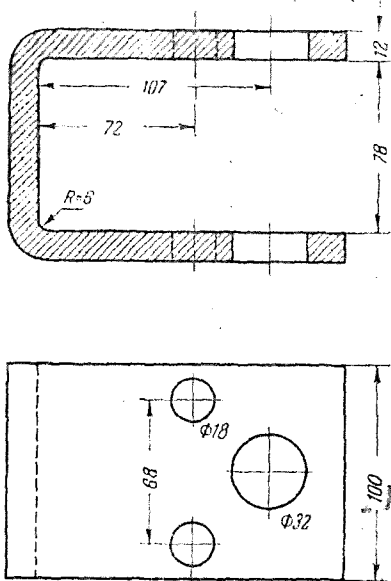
Скоба (материал — сталь 1010; размер заготовки 100×400 мм)
